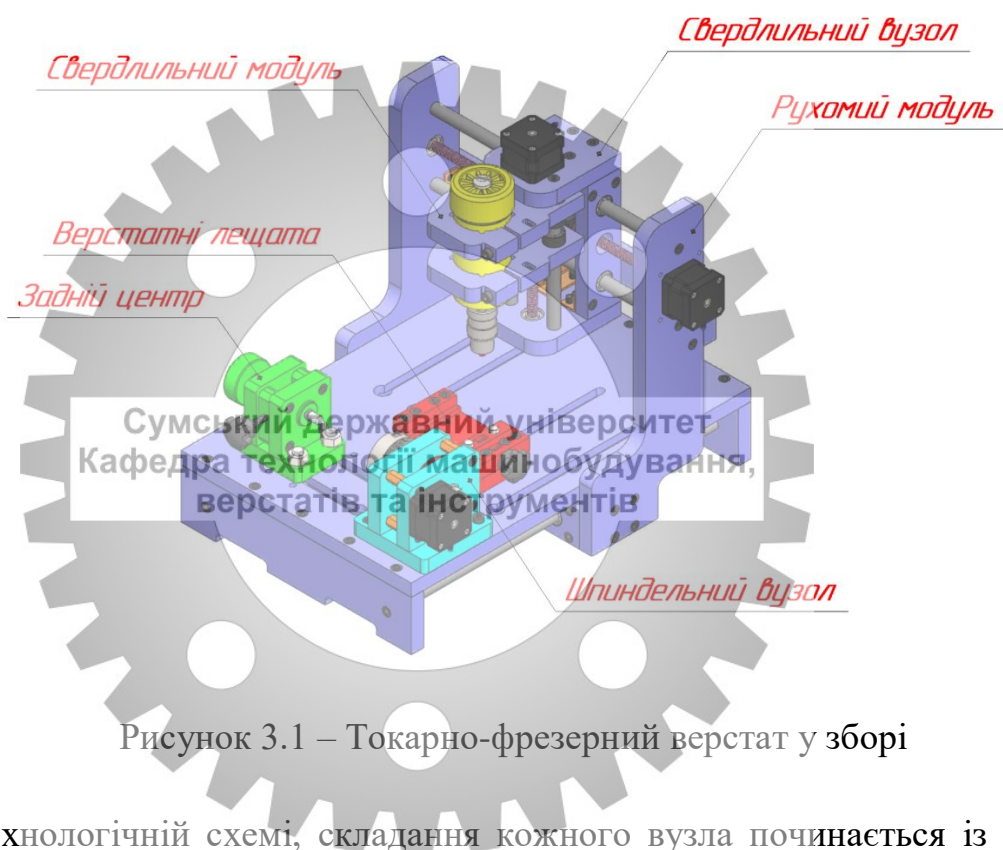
Токарно-фрезерний верстат у зборі
